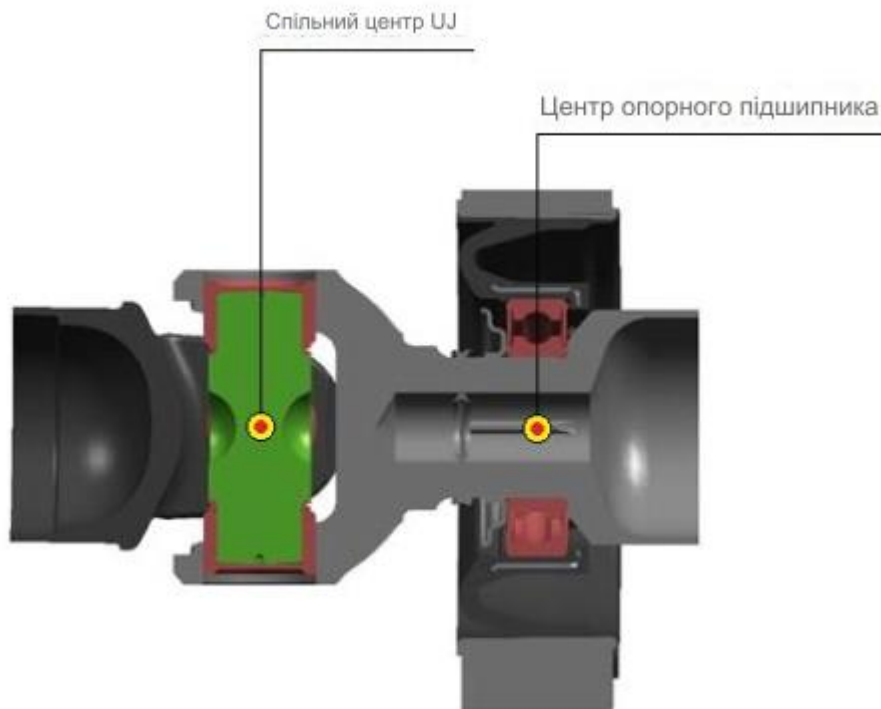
Положення універсального шарніра та опорного підшипника
